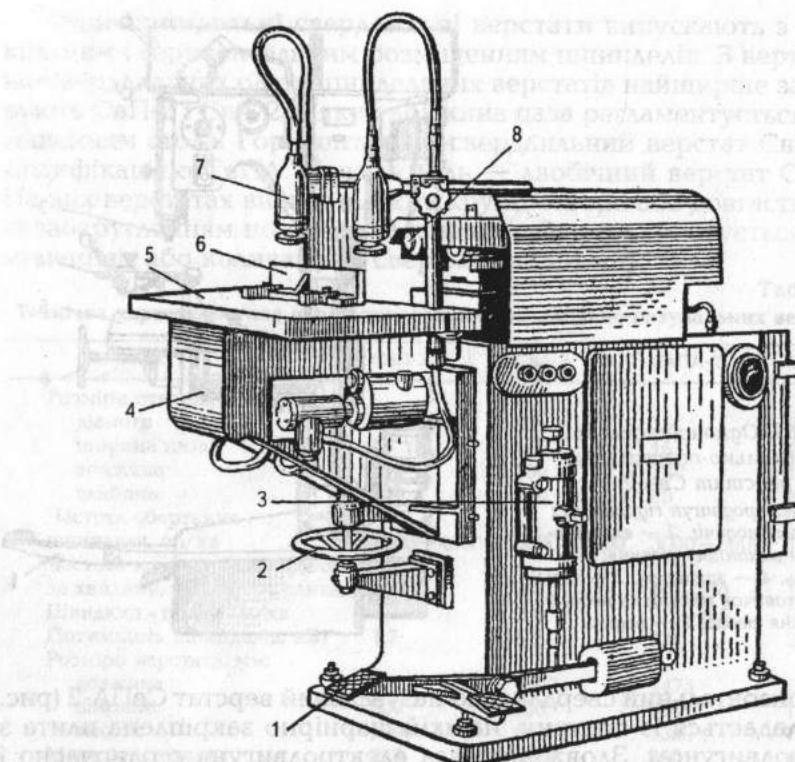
Свердильно-пазувальний верстат СвПА-2:
